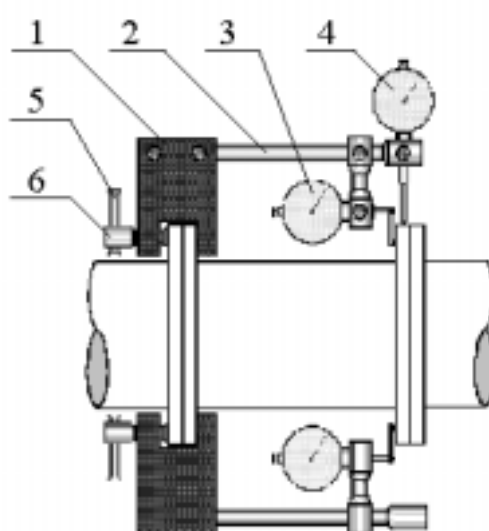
Прибор для центровки ПЦ-2: 1-струбцина; 2 - штанга; 3 - индикатор горизонтальный; 4 - индикатор вертикальный; 5 - рычаг винта; 6 – винт
